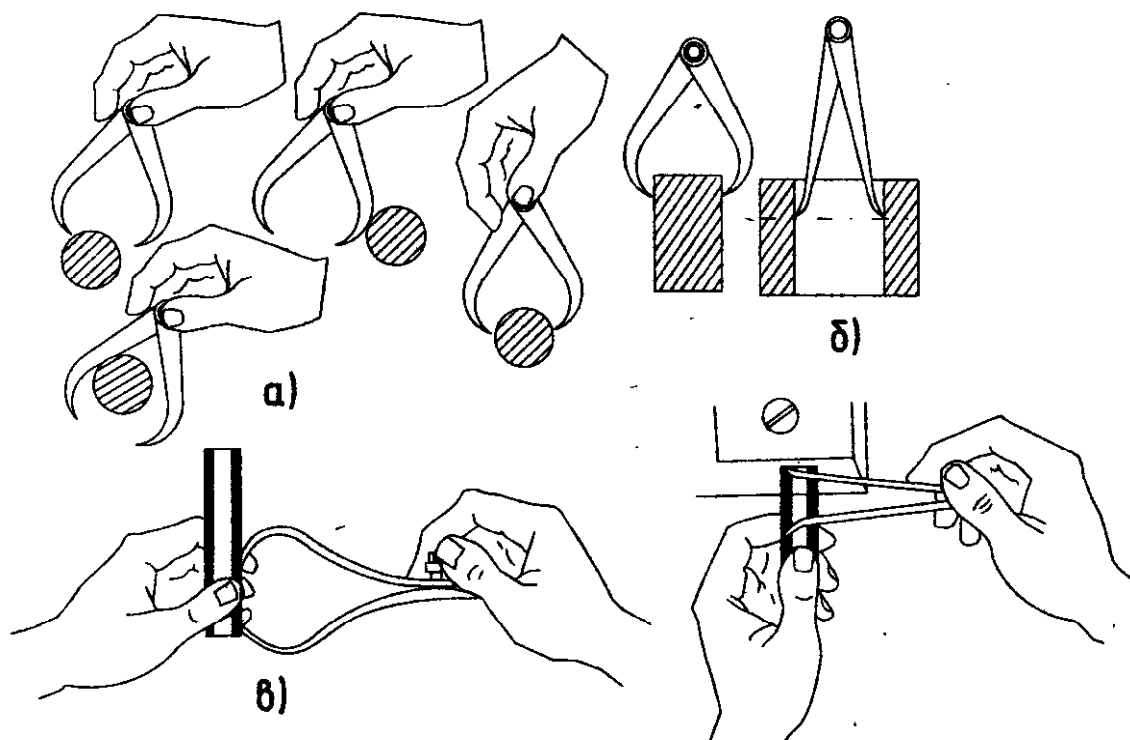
Приемы измерений детали кронциркулем и нутромером:
